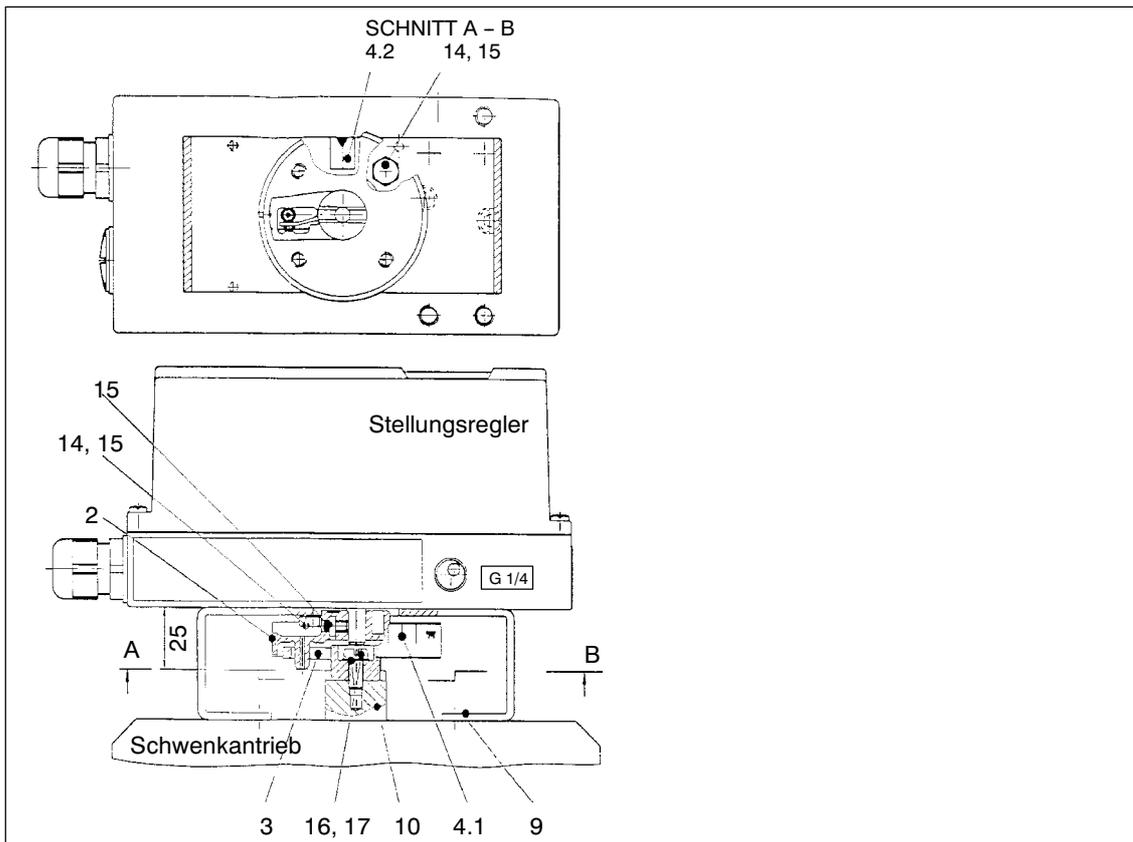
Montageablauf für druckfestes Gehäuse (Schwenkantrieb)
